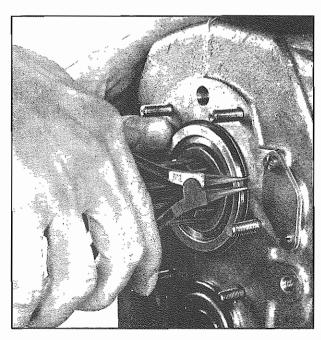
Estrarre l'anello di arresto Withdrawing out the stop ring
